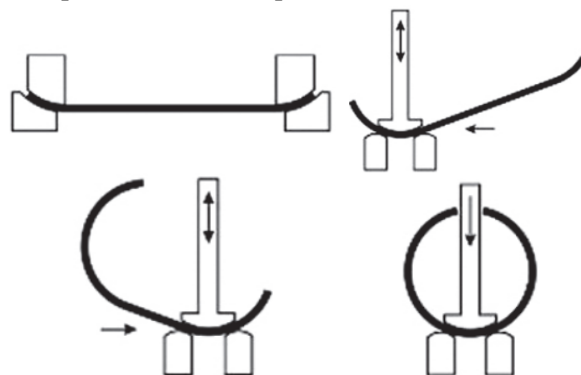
Постепенная формовка трубной заготовки штампами (JCOE)
